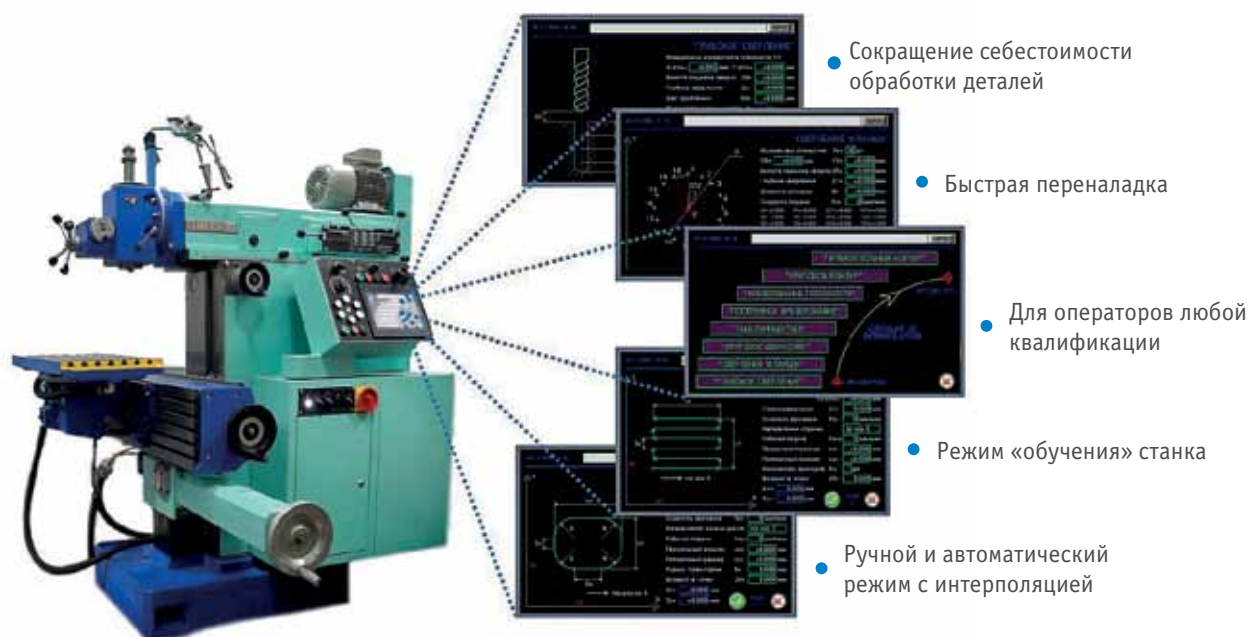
Фрезерный станок Mikron WF3 DP с оперативной системой управления
